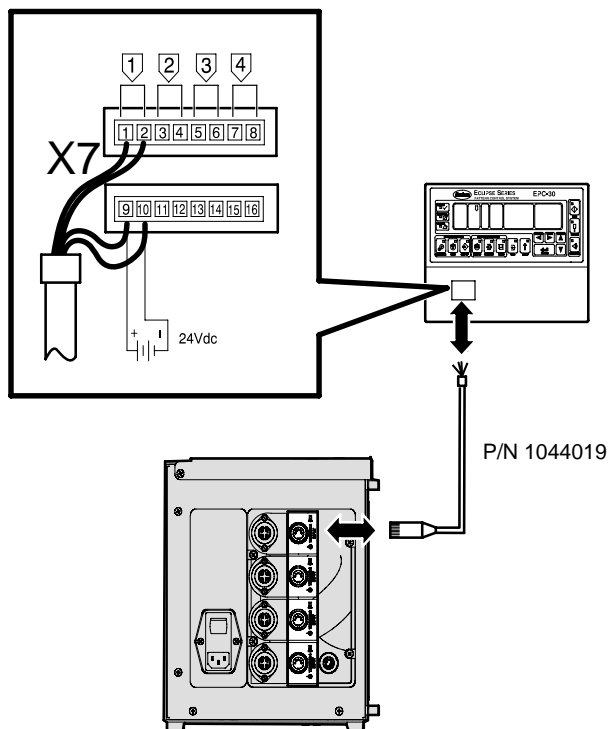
Collegamento di un EPC-30 agli e driver2, 3, 4 (nella figura il cablaggio di una pistola singola)
